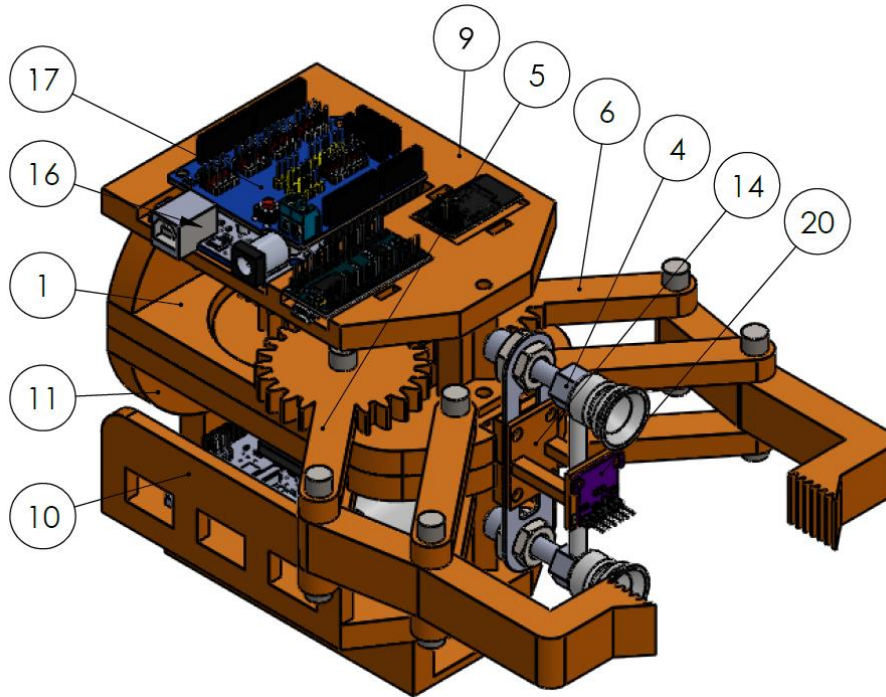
49. Vista isométrica izquierda herramienta ensamblada
